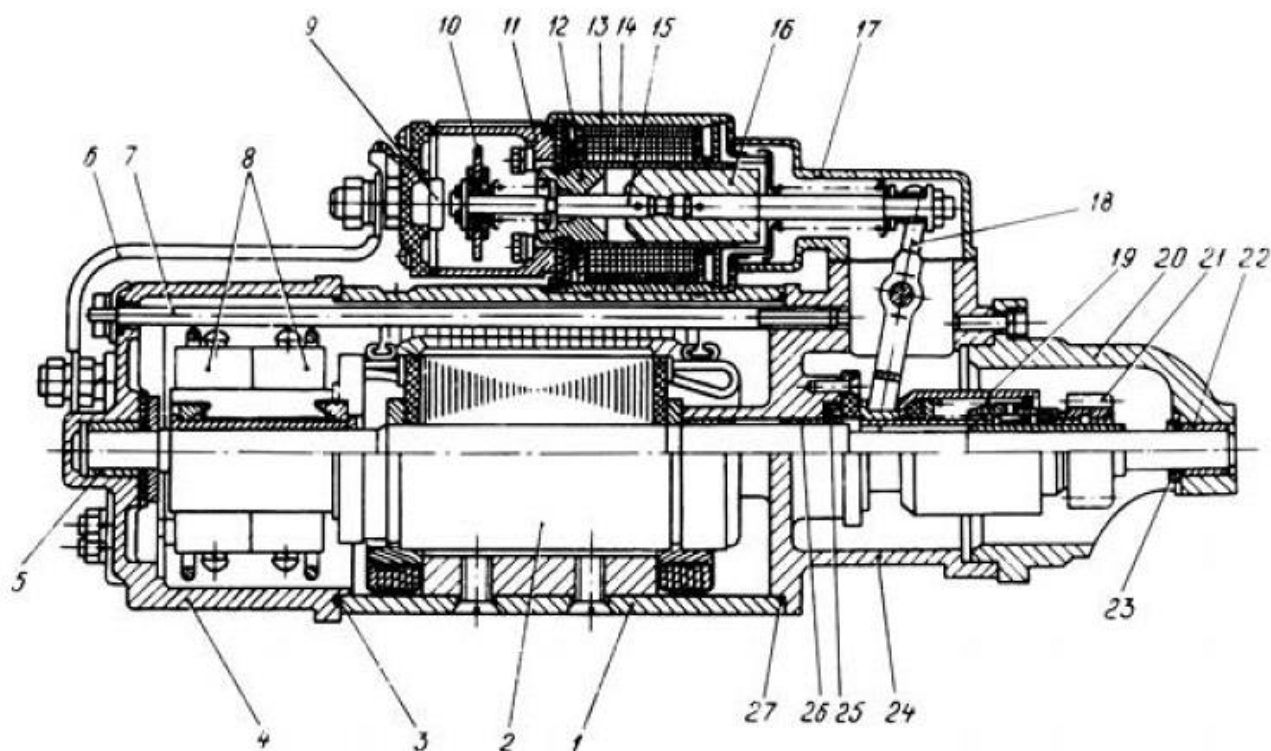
будова стартера СТ-25: 1 - корпус; 2 - якор; 3 - ущільнювальні кільця; 4 - кришка з боку колектора; 5 - передній підшипник; 6 - сполучна шина; 7 - стяжна шпилька; 8 - щітки; 9 - контактні болти; 10 - контактний диск; 11 - корпус реле; 12 - сердечник; 13 - утримуюча обмотка реле; 14 - втягує обмотка реле; 15 - шток якоря; 16 - якор реле; 17 - кожух; 18 - важіль приводу; 19 - привід; 20 - кришка з боку приводу; 21 - шестерня приводу; 22 - середній підшипник; 23 - шайба; 24 - корпус приводу; 25 - сальник; 26 - задній підшипник.
